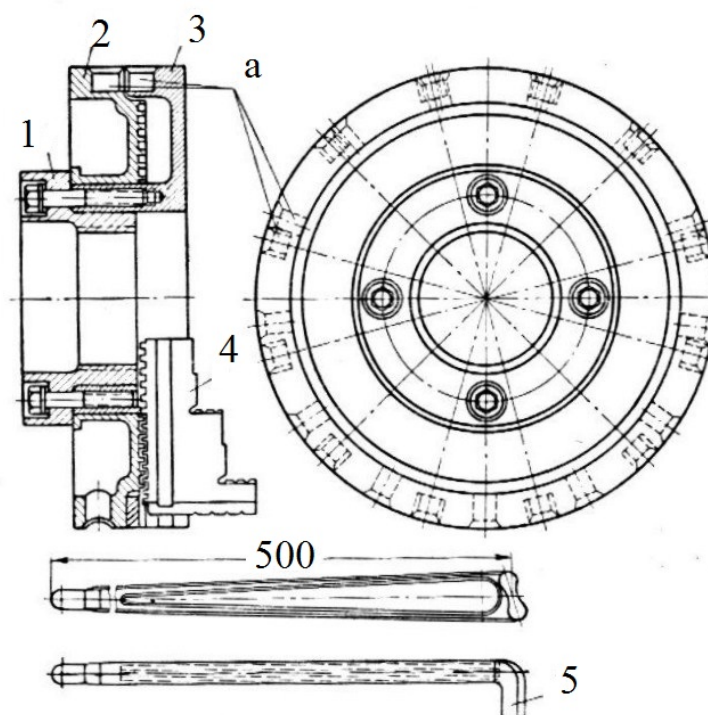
Универсальный трехкулачковый патрон без конической передачи (ключевой):
